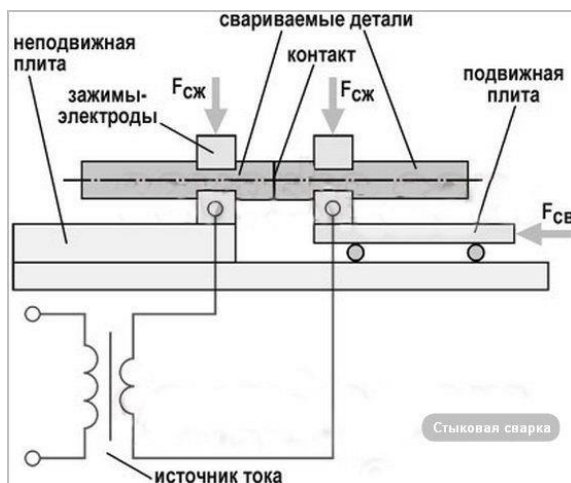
Контактная стыковая сварка оплавлением
